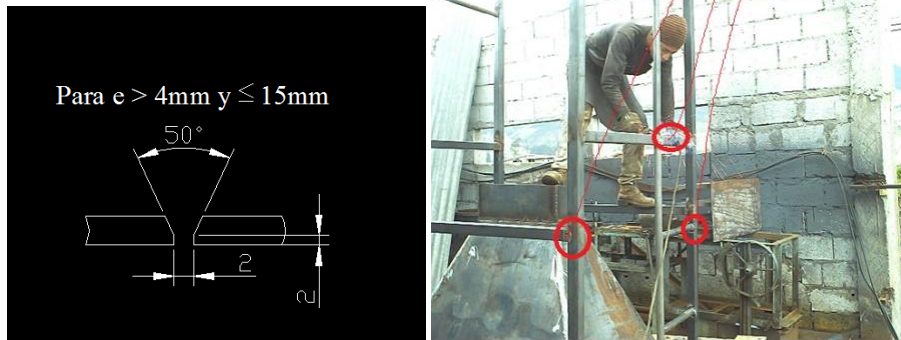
Proceso de Soldadura de la Tolva de Almacenamiento
